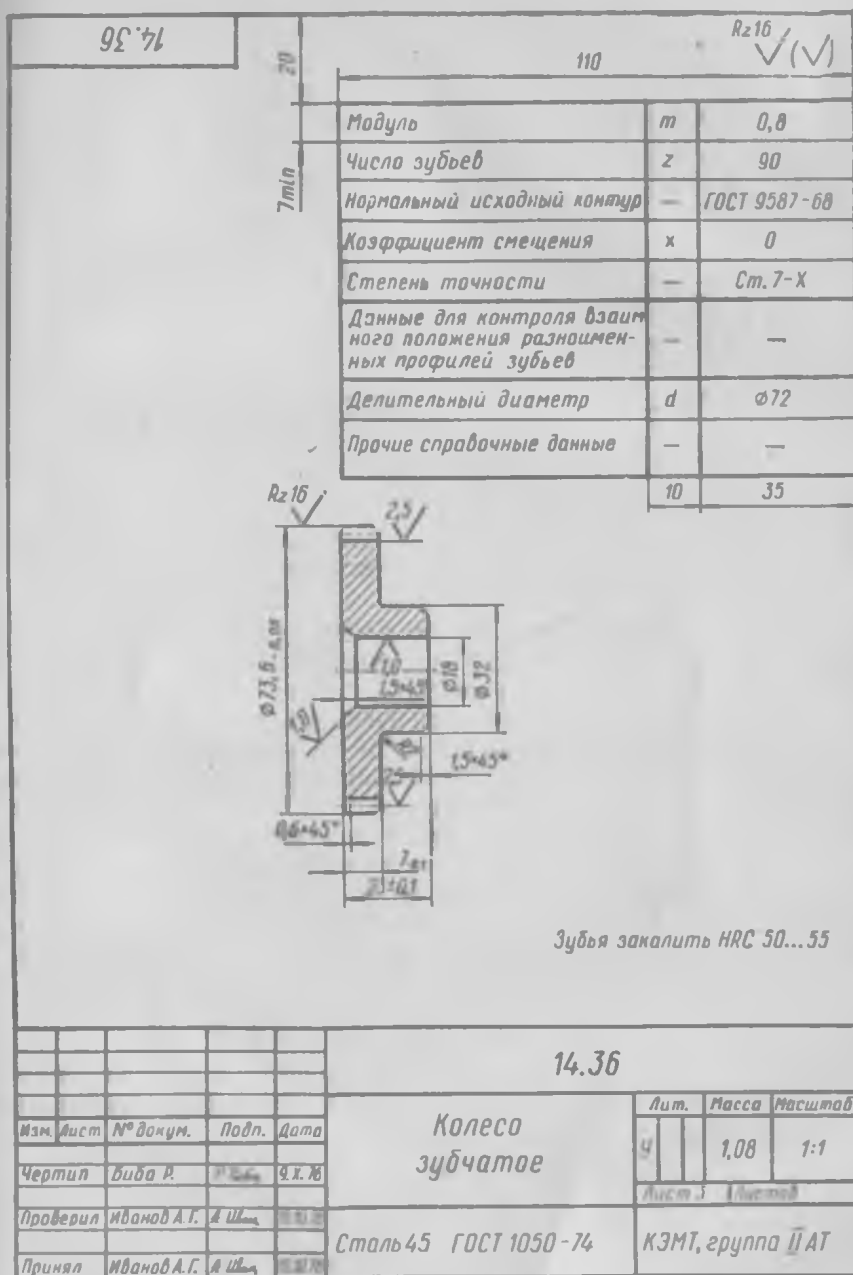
Рабочий чертеж зубчатого колеса (учебный)
